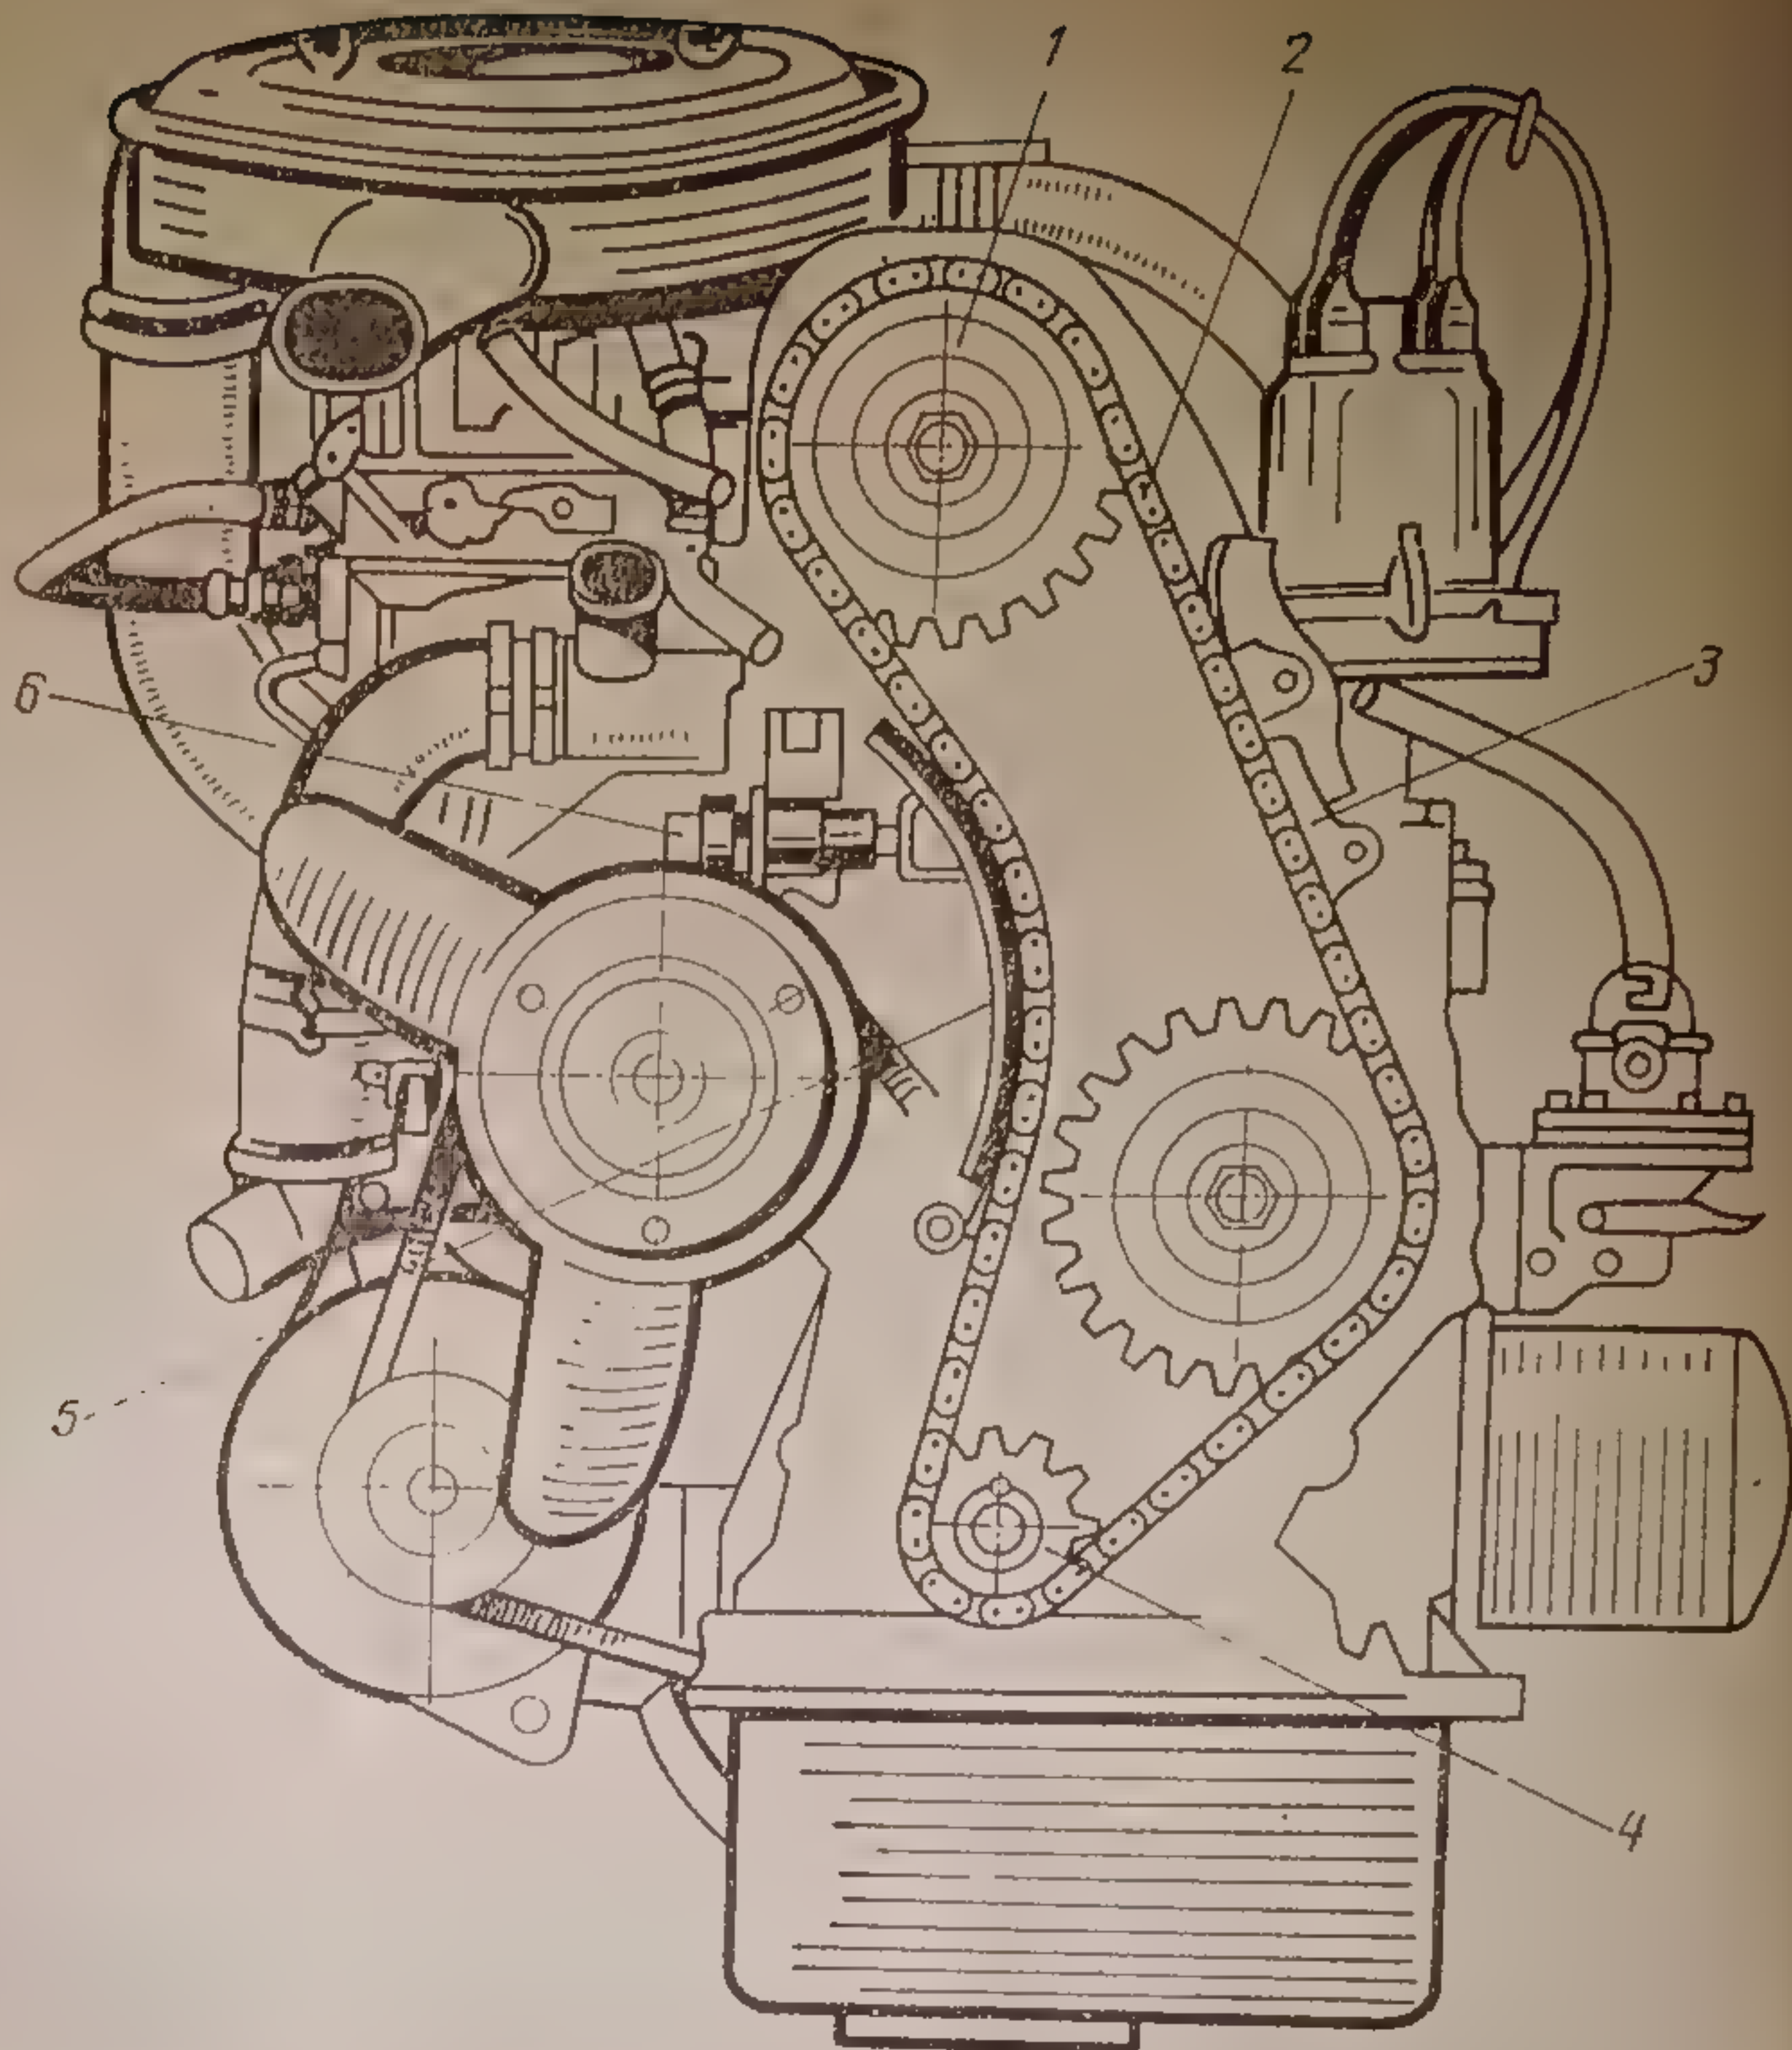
Цепной привод распределительного вала двигателя: 1 — ведомая звездочка распределительного вала; 2 — цепь привода распределительного вала; 3 — успокоитель цепи; 4 — ведущая звездочка; 5 — башмак натяжителя цепи; 6 — колпачковая гайка натяжителя цепи
